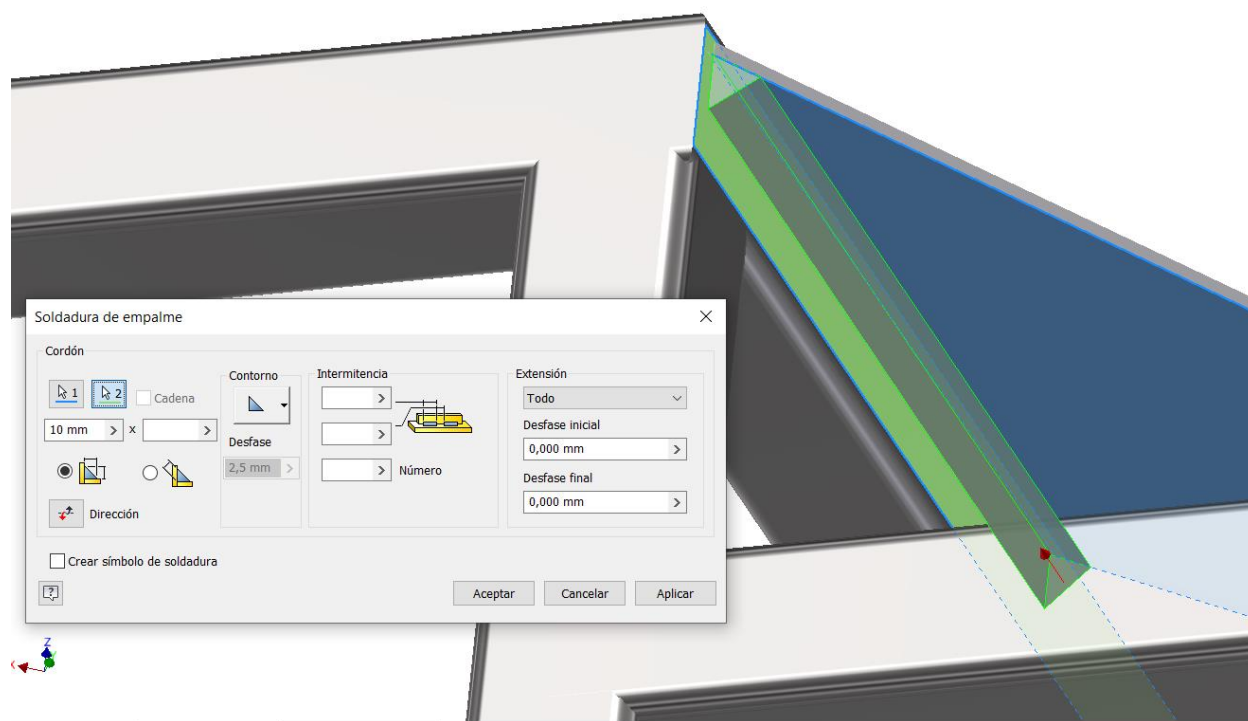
Soldadura de la placa de refuerzo del tubo de dirección con el chasis.
